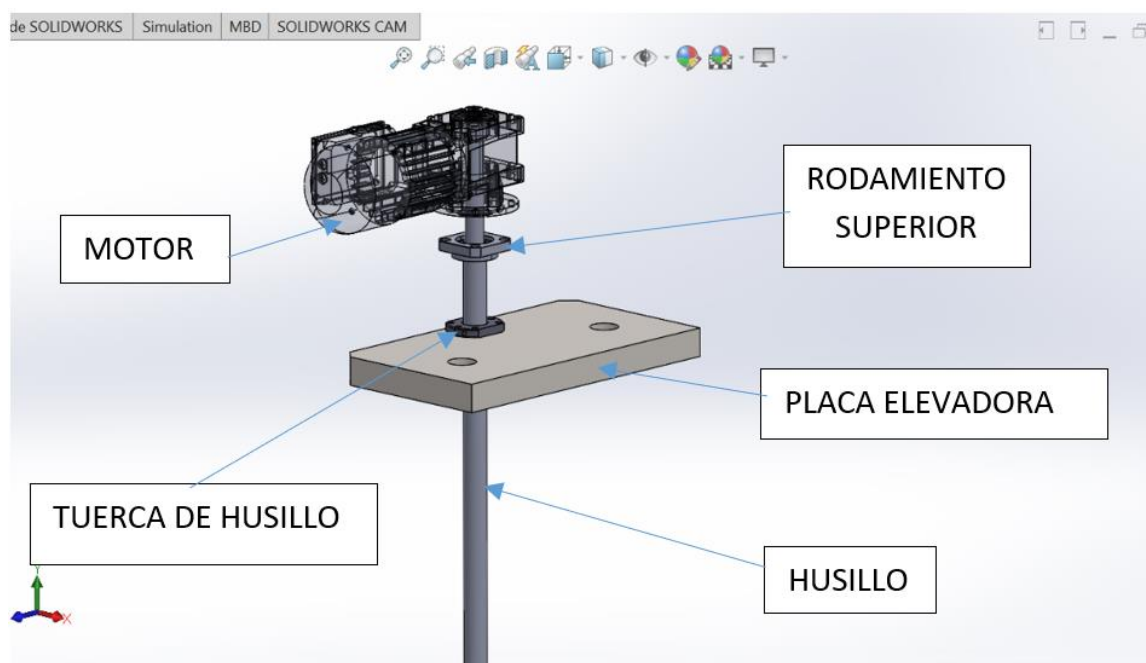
Parte superior del sistema de elevación del conjunto de masas
